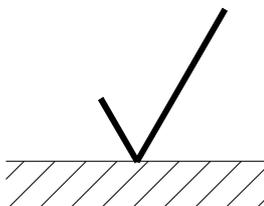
símbolo de estado de superfície que permite retirada de material.
